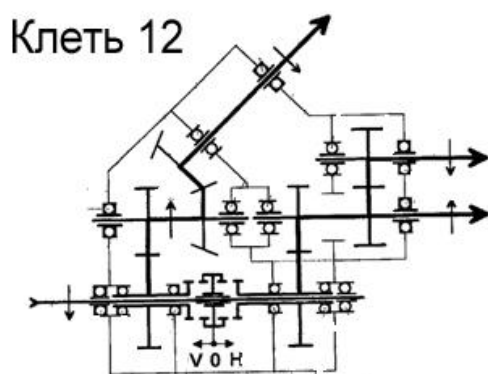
Кинематические схемы универсальных комбинированных редукторов непрерывного прокатного стана
